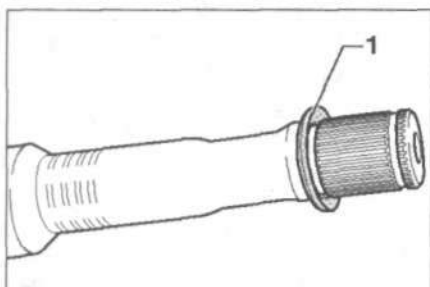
Установочное положение тарельчатой шайбы на внутреннем шарнире:
